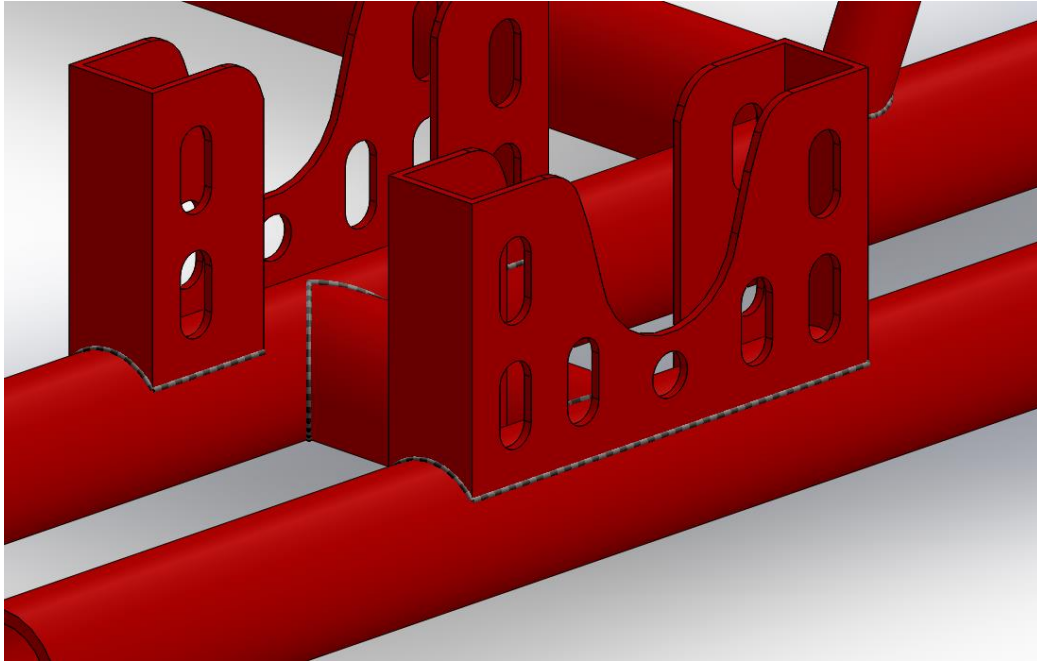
detalle cordones de soldadura. Fuente: propia.
